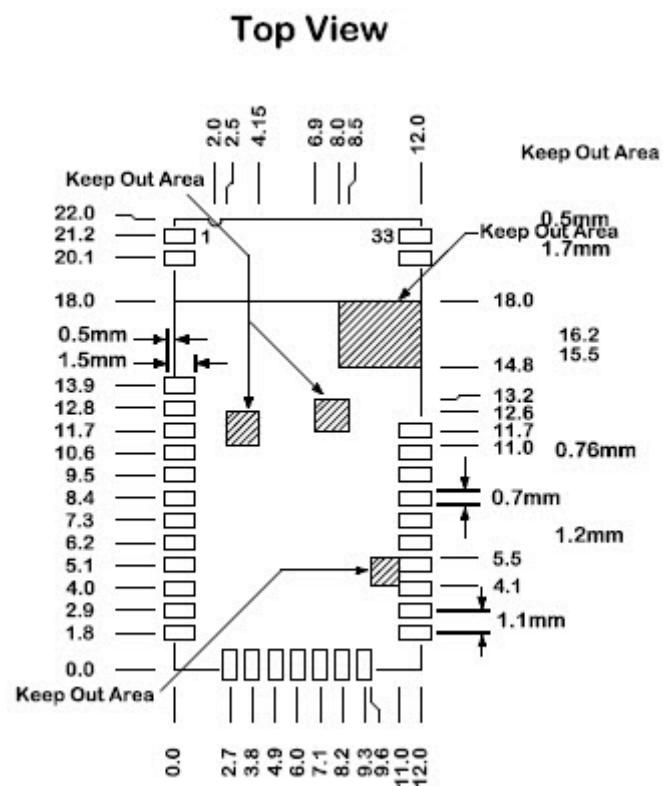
建议的 BM70BLES1FC2 PCB 尺寸
